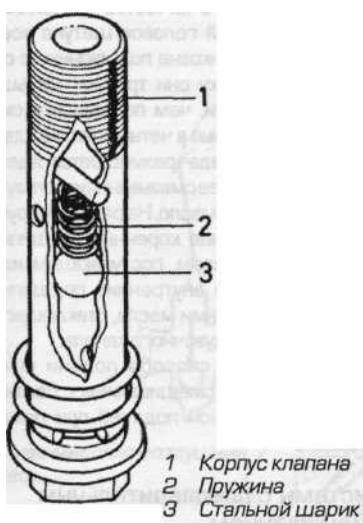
Перепускной клапан в виде болта корпуса фильтра
